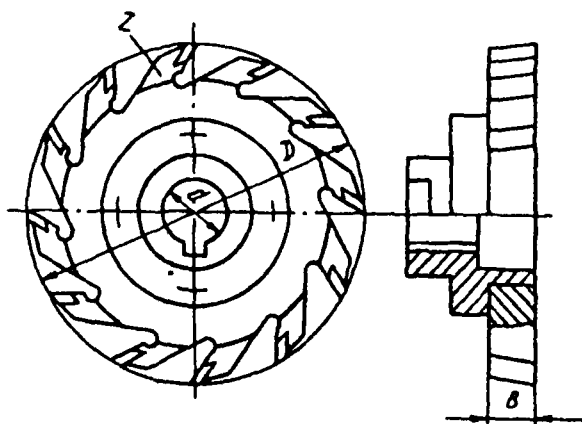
Пример фрезы для обработки окон (фасонная сборная с ножами, оснащенными твердым сплавом)
